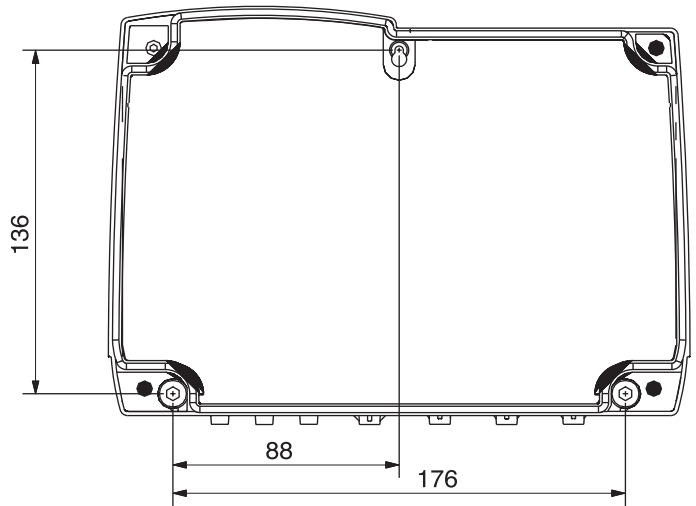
Plantilla para taladrar (dimensiones en mm)
